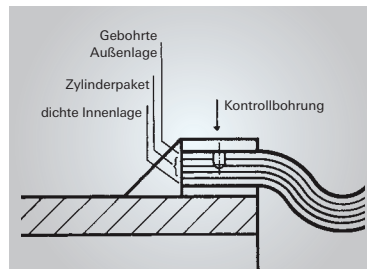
Schweißnaht und Kontrollbohrung
